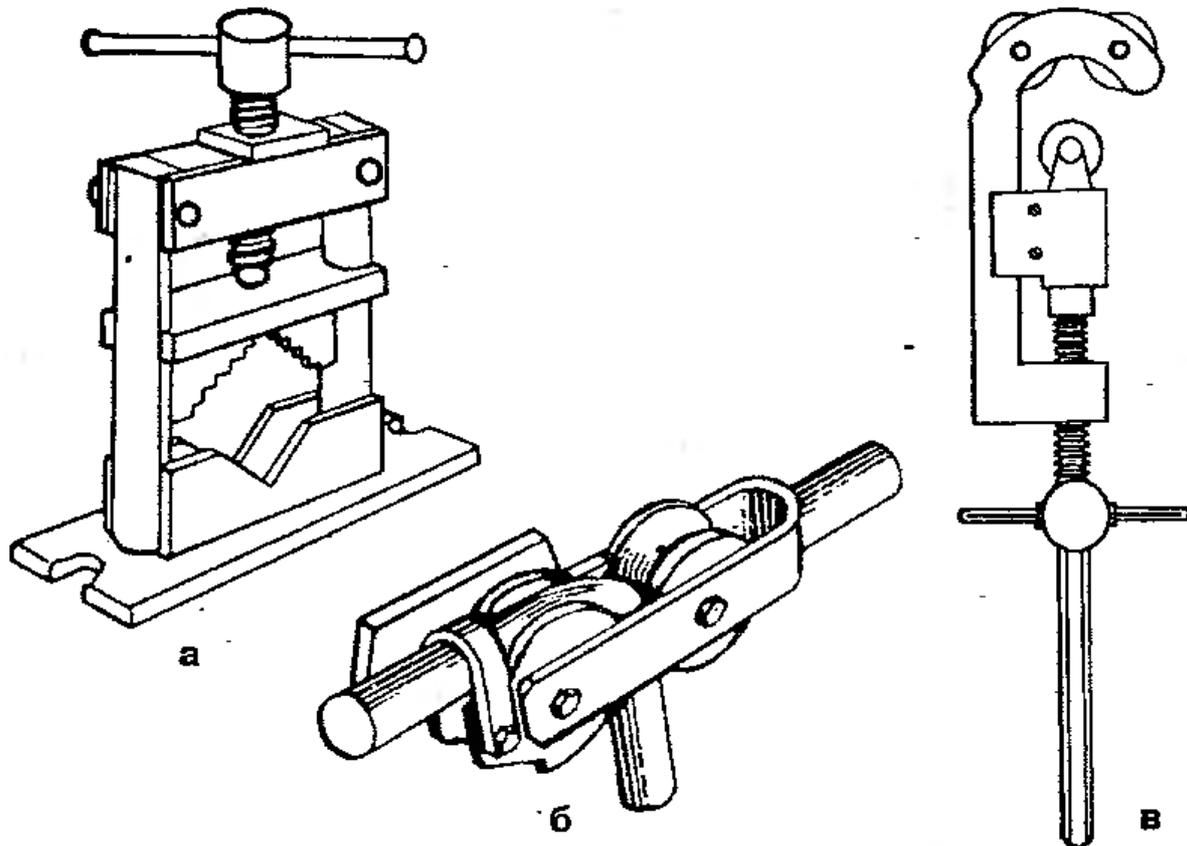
Инструменты для работ с трубами: а — прижим; б — стационарный трубогиб Вольнова; в — труборез
